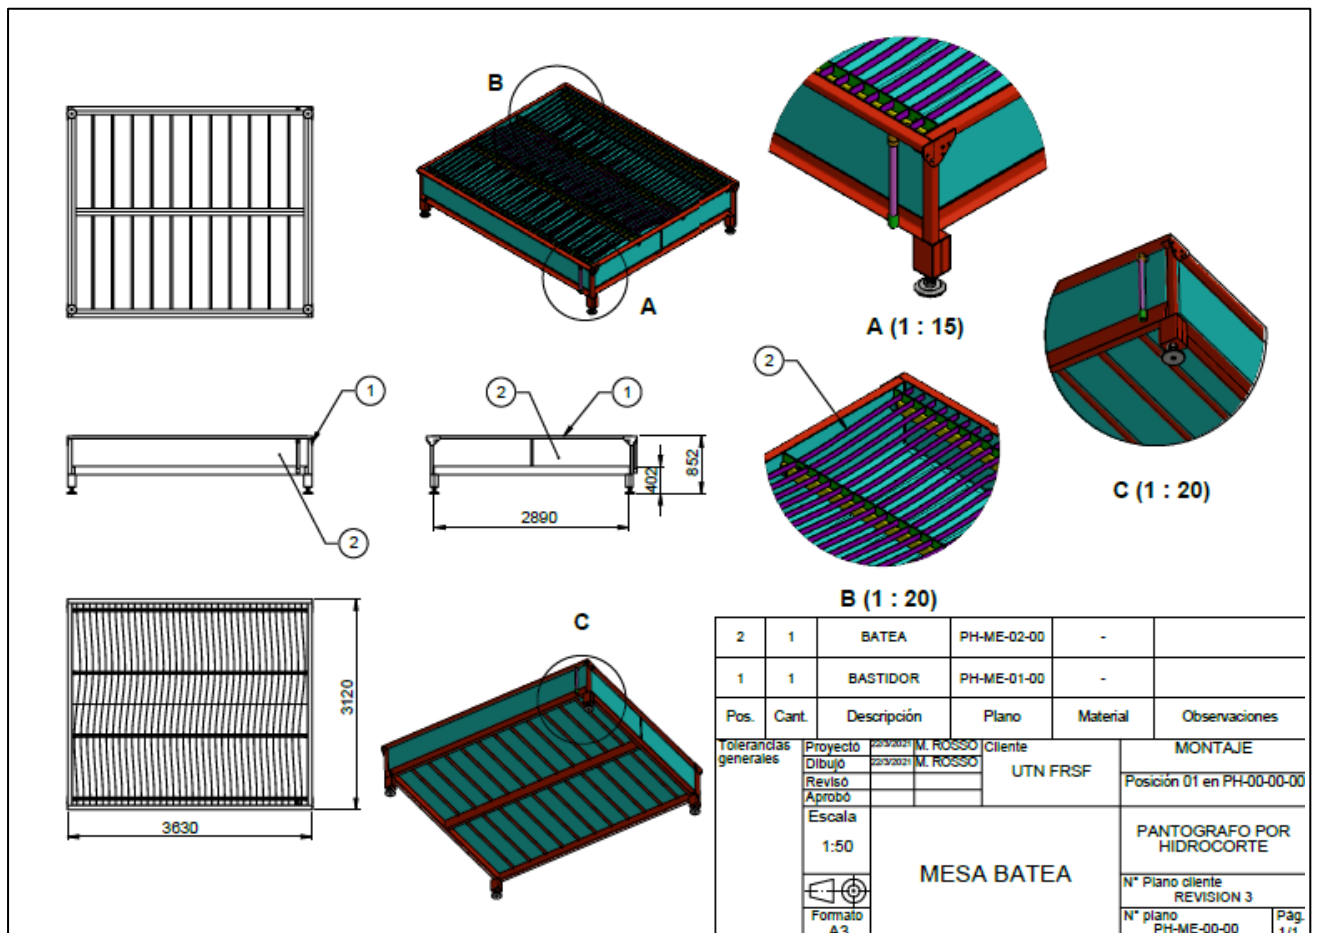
Planos esquemáticos Mesa-Batea (ver "anexo 6- Planimetría")
